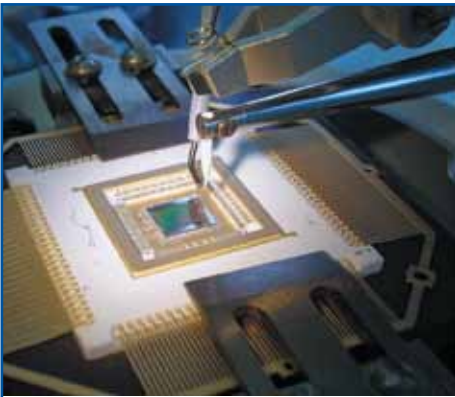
Сварочный микроинструмент и электрод разрядника в установке термовзвучивающей микросварки
